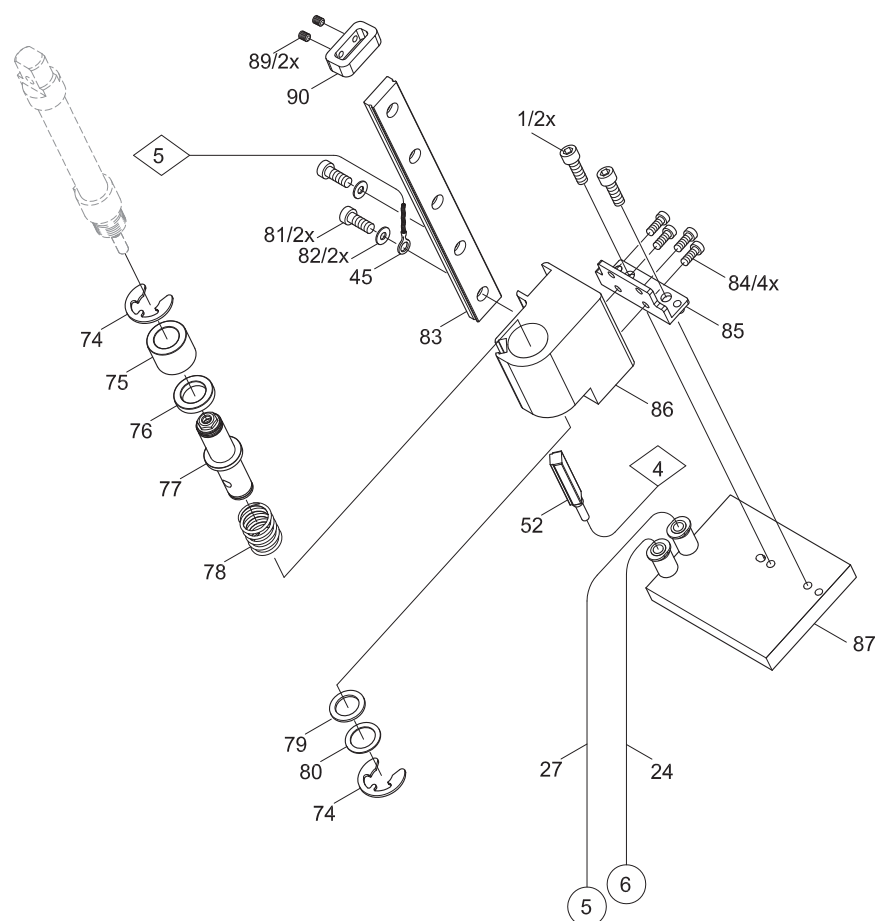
Zylinderbaugruppe X/Y - Ersatzteil
